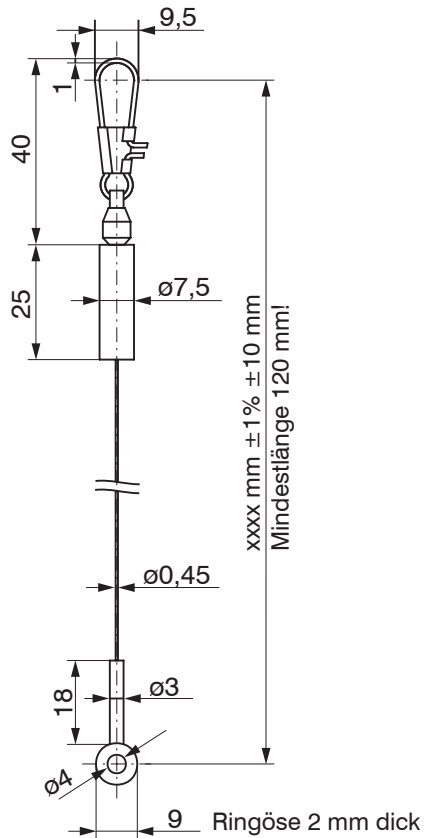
Seilverlängerung WE-xxxx-CLIP, Abmessungen in mm
